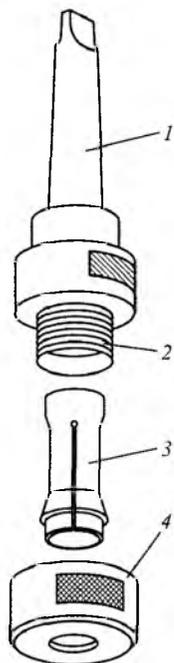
Цанговый сверлильный патрон: 1 – хвостовик; 2 – цилиндрическая часть; 3 – разрезная втулка; 4 – кольцо
